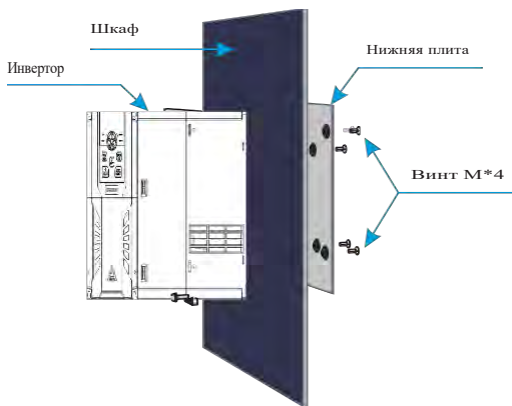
Чертеж установки пластиковой конструкции через стену
